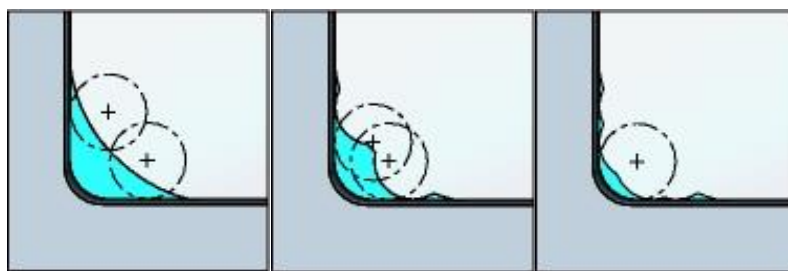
Оброблення кутів плунжерним фрезеруванням
